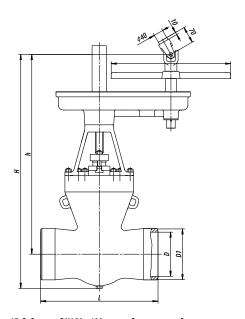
Задвижка DN150...400 с цилиндрическим редуктором
